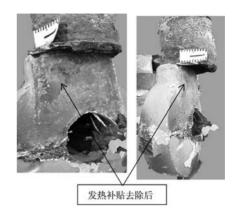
发热补贴去除后的铸件表面状态 Fig. 11 Conditons of casting surfaces after removal of exothermic pads
